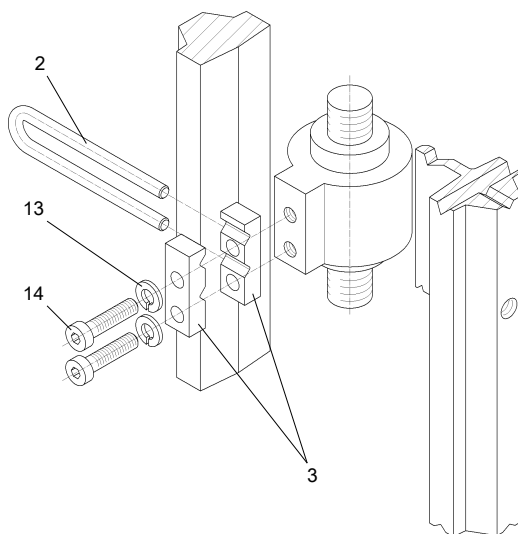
Монтаж приспособления для контроля хода на шпинделе привода
